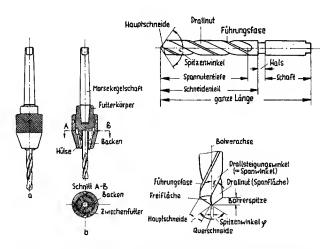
Bohrwerkzeuge; links Dreibocken-Bohrfutter mit konischem Schaft, rechts oben Spiralbohrer mit Bezeichnung der Einzelheiten und rechts unten die Bohrerspitze mit den entsprechenden Winkeln
